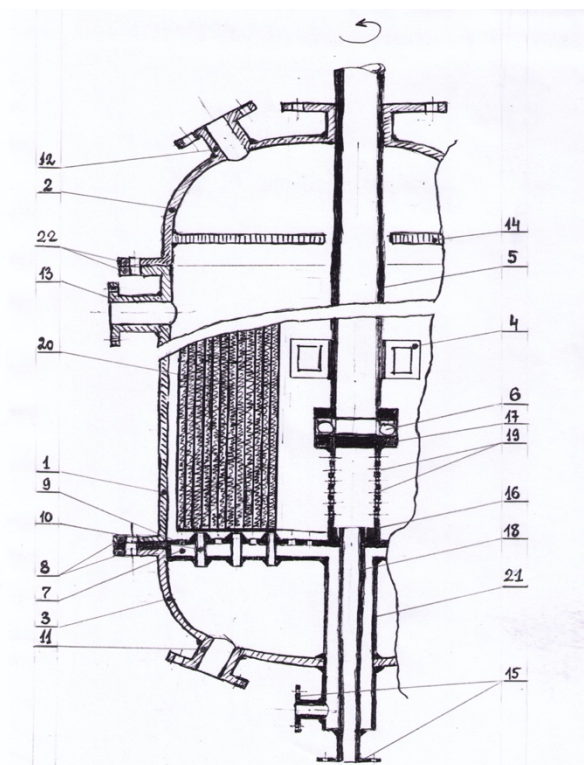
Трёхфазный каталитический реактор смешения. 1 — цилиндрический корпус; 2 — эллиптическая крышка; 3 — эллиптическое днище; 4 — внутренняя мешалка; 5 — вал внутренней мешалки; 6 — подшипник; 7 — полая тарелка; 8 — нижнее фланцевое соединение; 9 — отверстия для ввода газообразных реагентов; 10 — сквозные отверстия для ввода жидкой фазы; 11 — штуцер для ввода жидкой фазы; 12 — штуцер для вывода газообразных продуктов; 13 — штуцер для вывода жидкой фазы; 14 — пеногаситель; 15 — штуцеры для подвода газообразных реагентов; 16 — патрубок; 17 — опора для подшипника; 18 — труба малого диаметра; 19 — дополнительные отверстия для ввода газообразных реагентов; 20 — кольцевой каталитический блок; 21 — труба большого диаметра; 22 — верхнее фланцевое соединение
